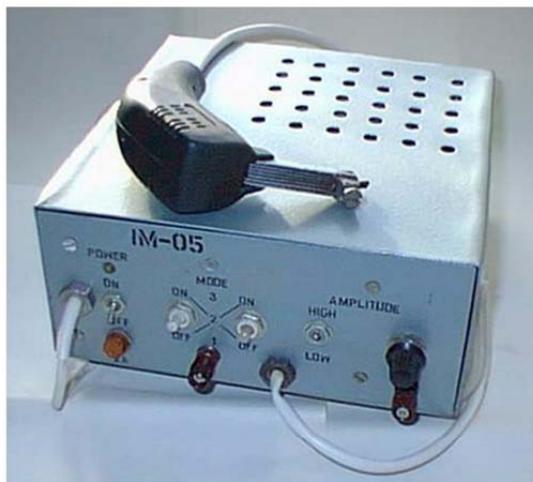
Малогабаритная установка для ручного ЭИЛ типа ИМ-05
